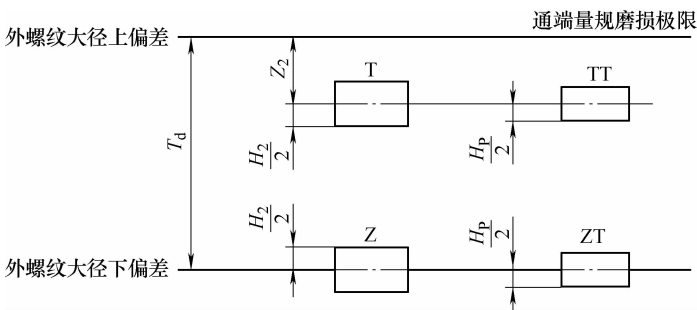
检验工件外螺纹大径用的光滑极限量规尺寸公差带图
